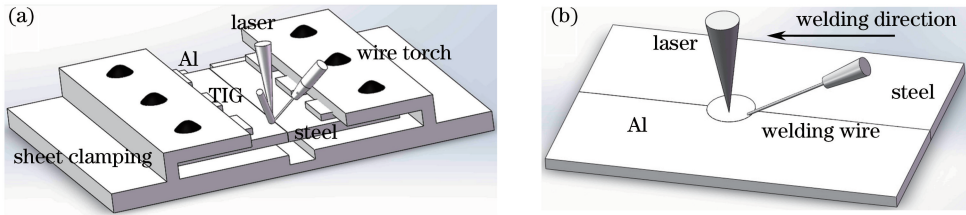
TIG 电弧辅助激光填丝熔钎焊示意图。(a) 焊接总示意图；(b) 焊丝位置
